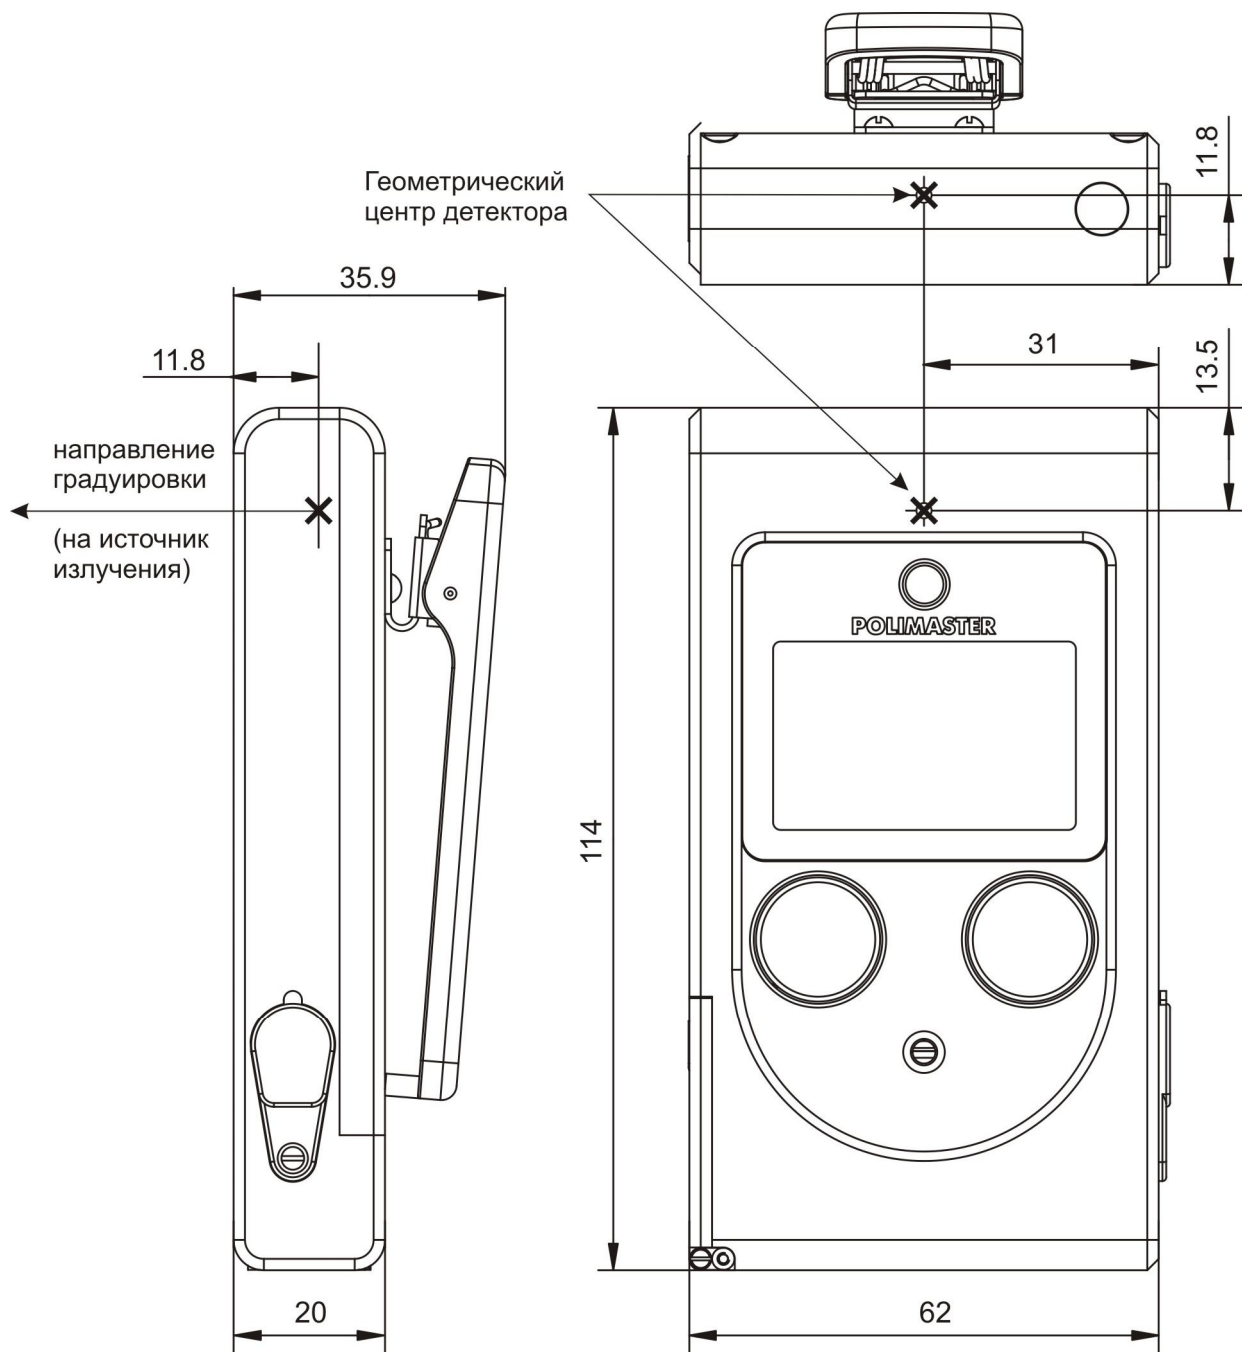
Габаритные размеры, расположение геометрического центра детектора прибора, направление градуировки
